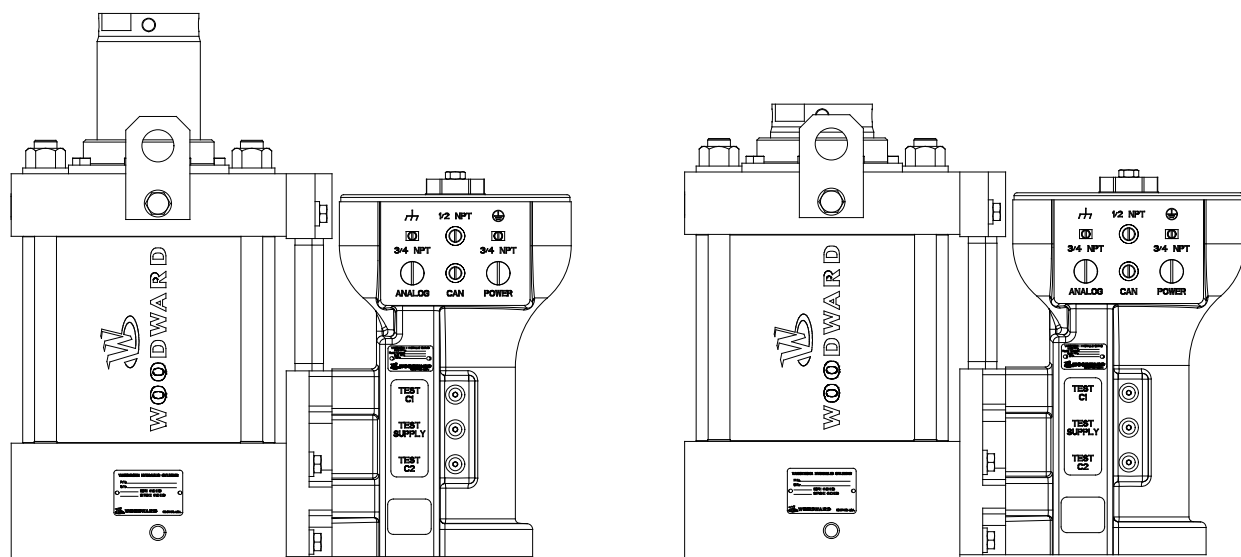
с. Положение гидравлического стержня для различных версий цилиндров
